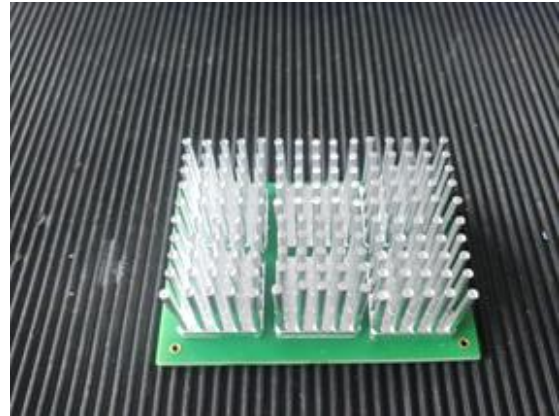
Ungefräste Heat Sinks auf der Unterseite
